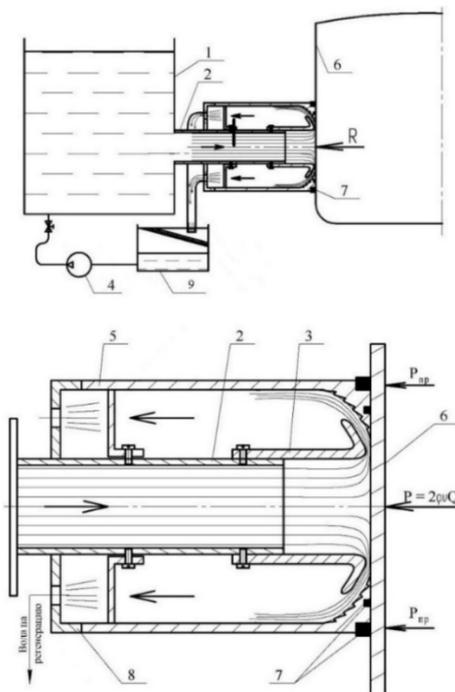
Устройство для очистки от коррозии судовых стальных поверхностей:
